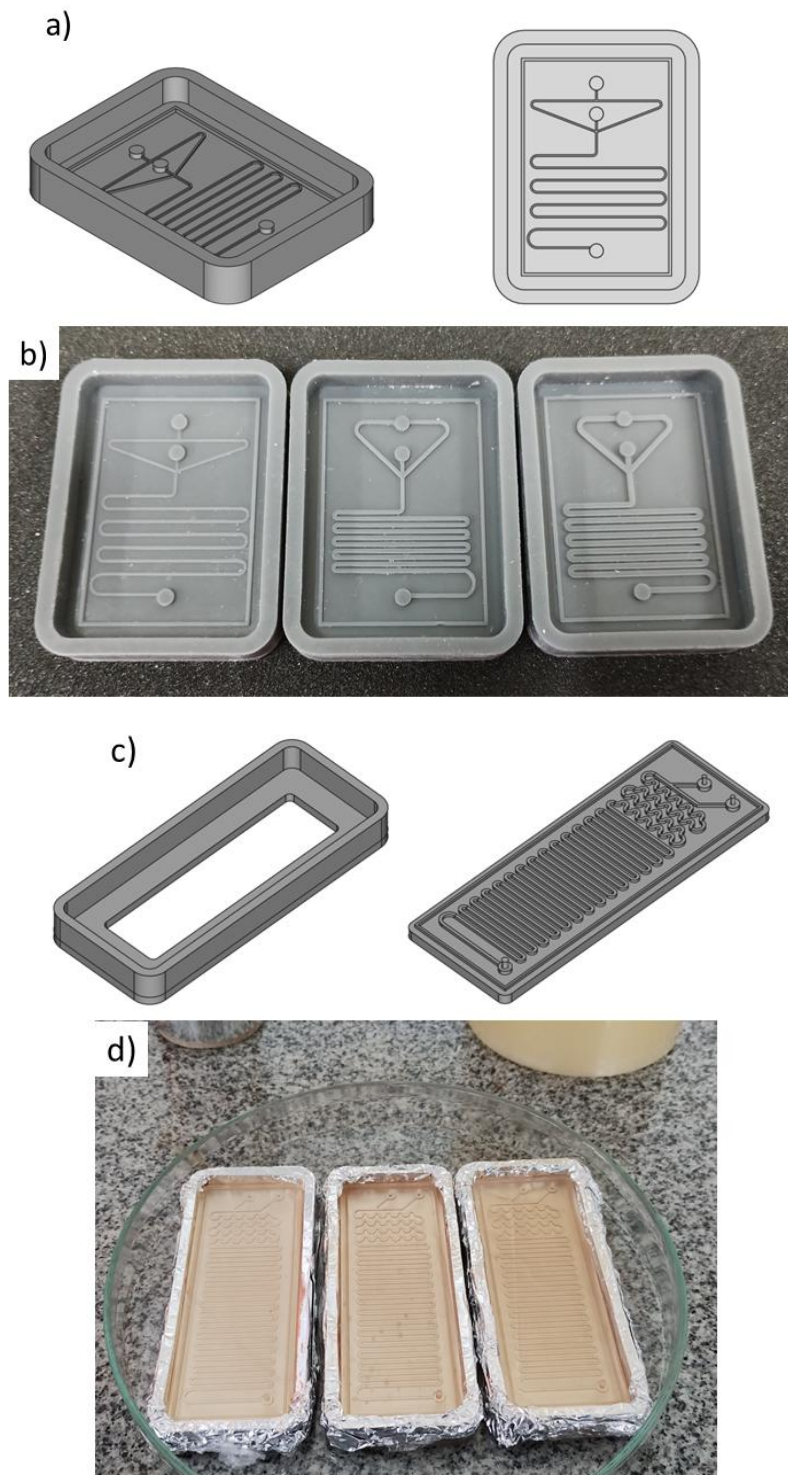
Modelos de moldes impressos; (a) e (c) imagens do projeto CAD do (b) molde simples em uma parte com os canais em diferentes tamanhos e arquitetura genérica, (d) molde em duas partes sendo um suporte e uma placa com o desenho dos canais, envolvidos com papel filme e folha de alumínio, respectivamente.
